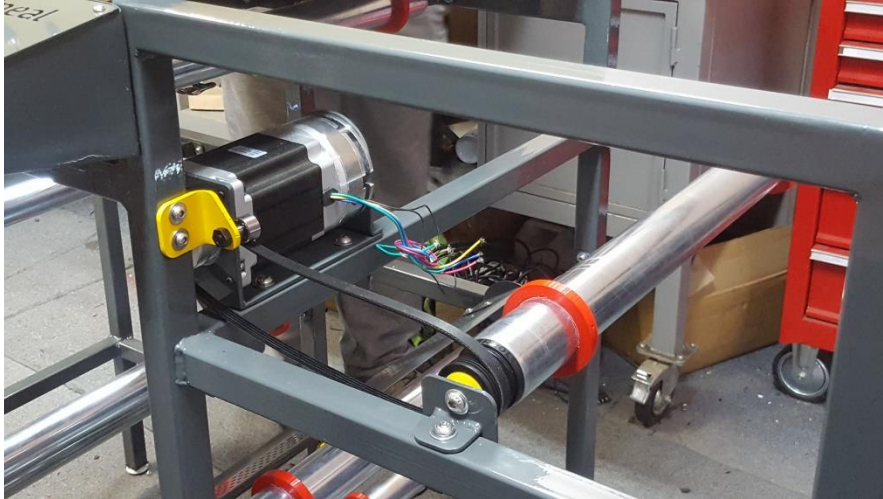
RODILLO SERIE 3500 Y MOTOR INSTALADOS EN PROTOTIPO
